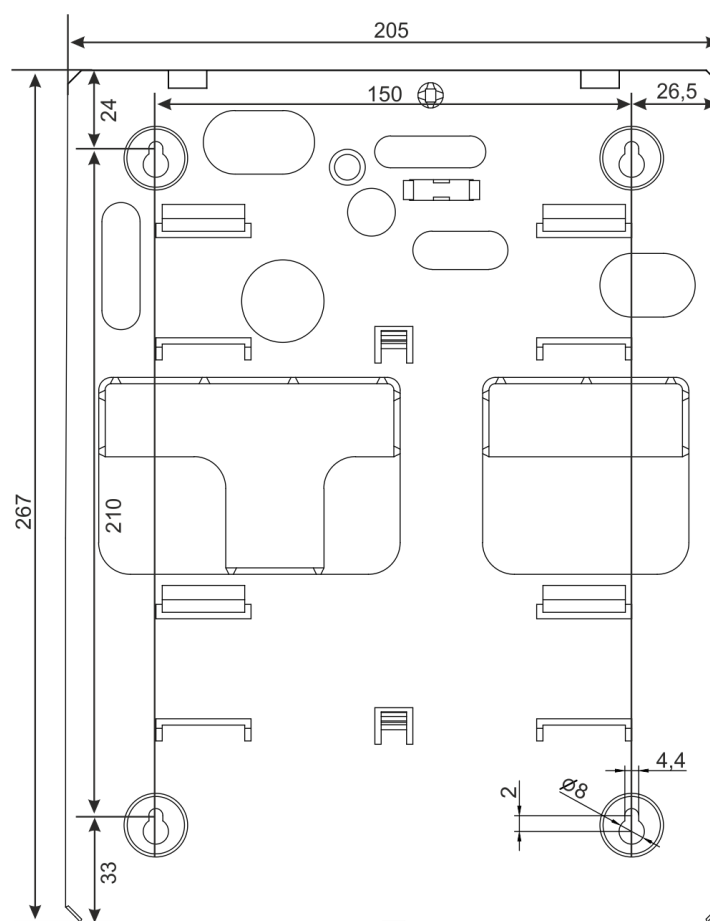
Установочный чертеж основания корпуса ППКО серии «А24» и бокса аккумуляторного БА-18
